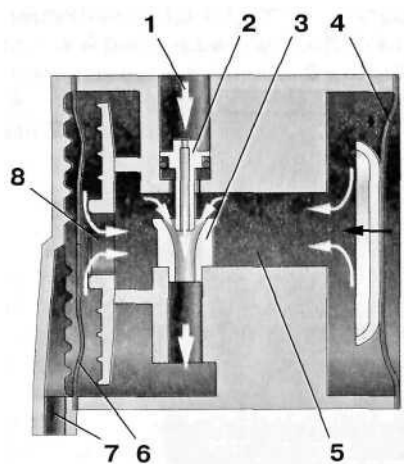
Общий вид и схема подключения редуктора-испарителя Vialle
